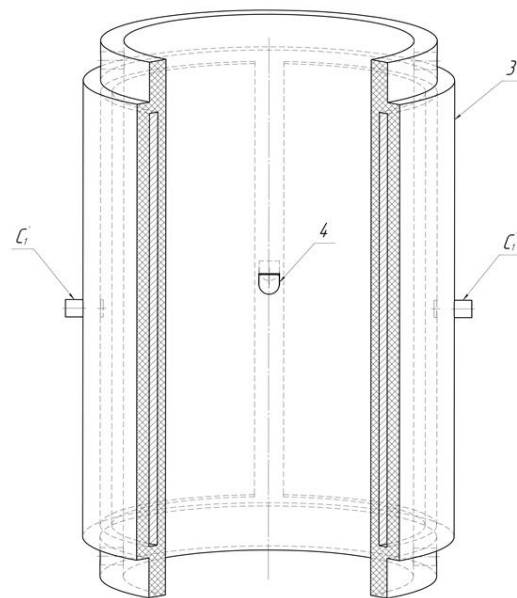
Общий вид конструкции полуцилиндрического ёмкостного датчика-дозатора
